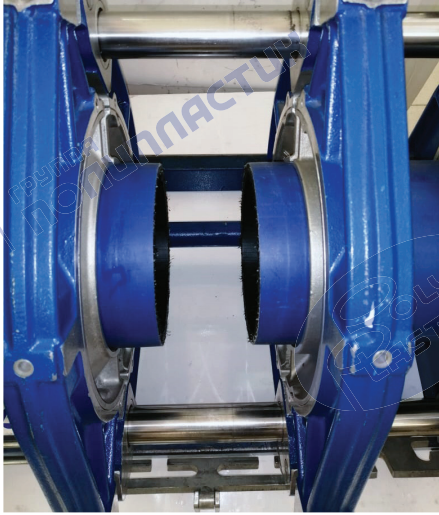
Трубы МУЛЬТИПАЙП, установленные в центратор сварочной машины
